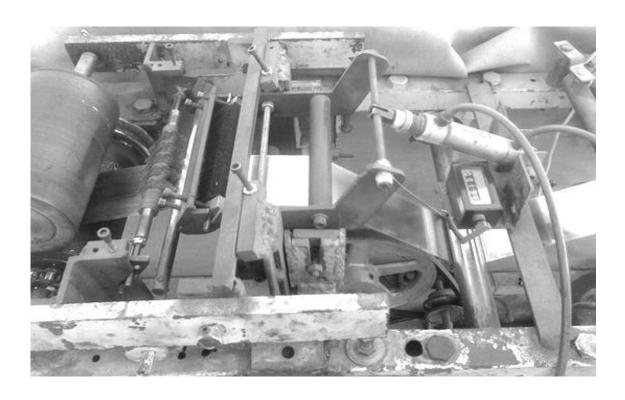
Pistón accionador de no corte cada 90 cm.
